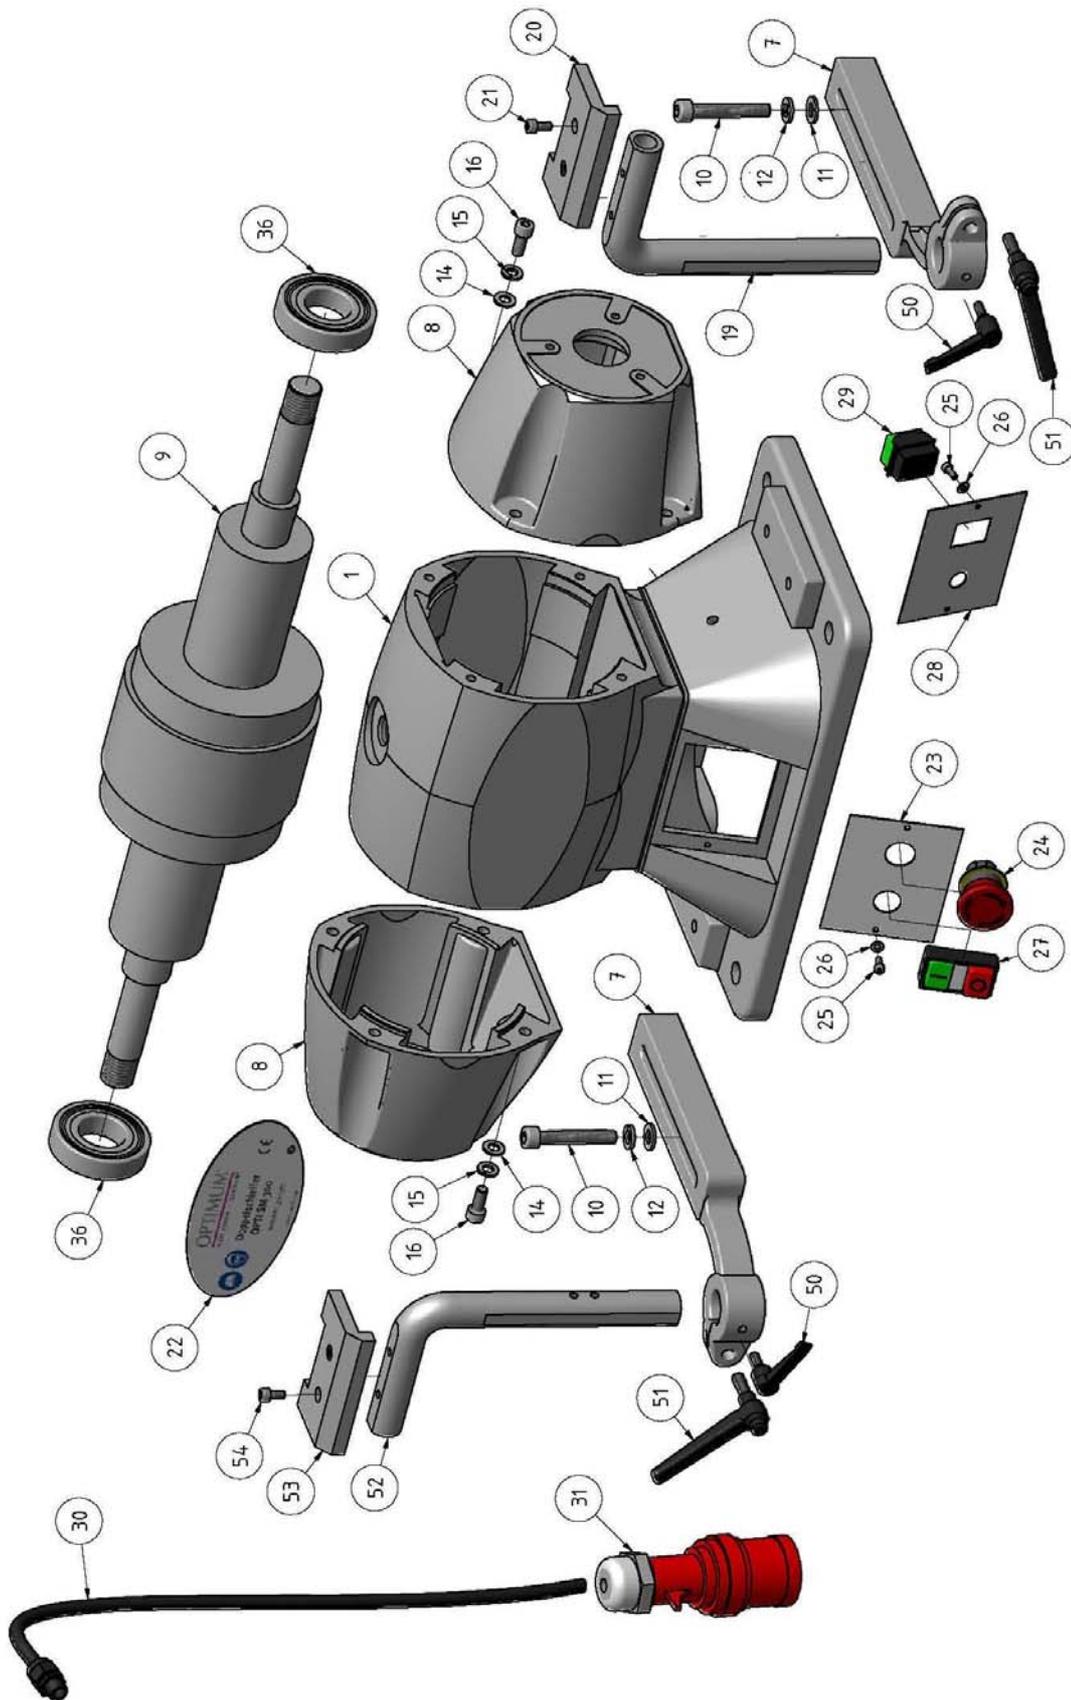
Ersatzteilzeichnung 2 von 2 - Drawing spare parts 2 of 2
